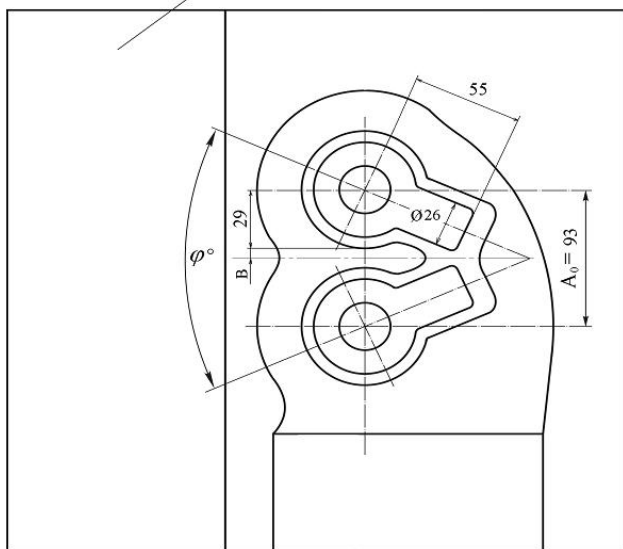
Эскиз компоновки штампа для спаренной штамповки поволок «рым-болт» с профилированием заготовок продольным изгибом
